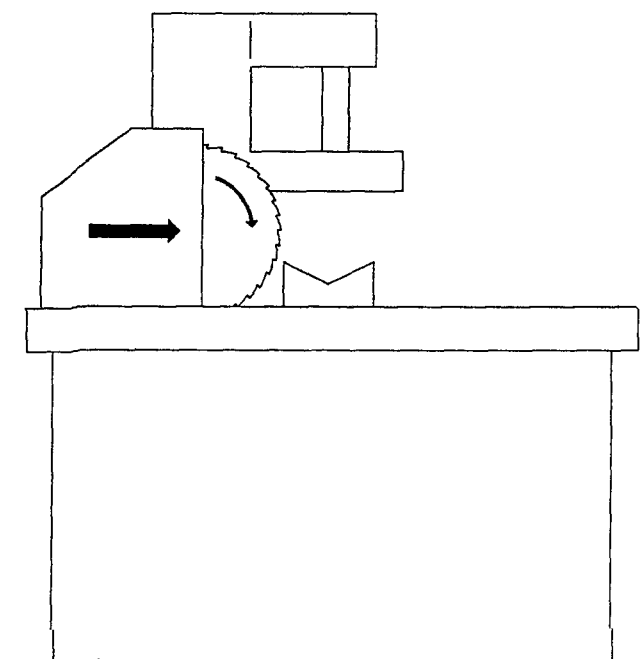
Круглопильный верстат для фронтального розпилювання
